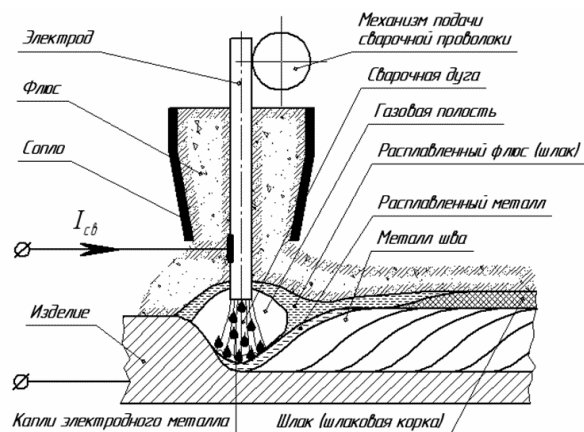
Сечение зон горения дуги при сварке под флюсом
